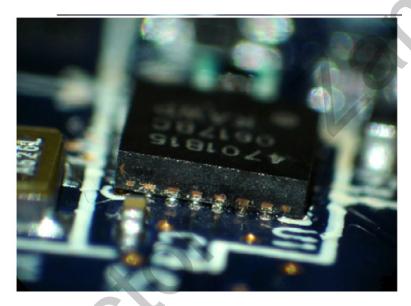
Soldadura del circuito integrado
